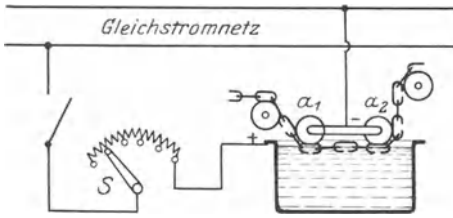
Schweißen von Ketten durch Elektrolyse.
